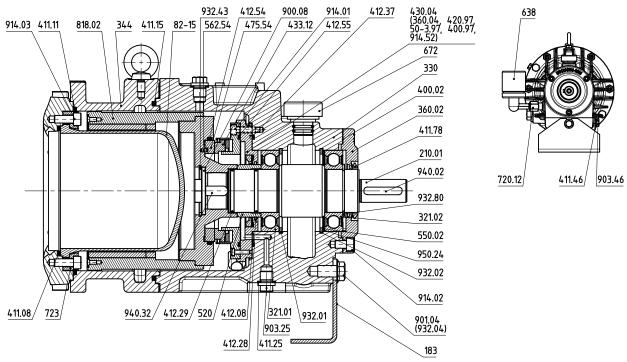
Исполнение подшипникового кронштейна с жидкой смазкой подшипников и смазываемым газом торцовым уплотнением в качестве защиты от утечек
